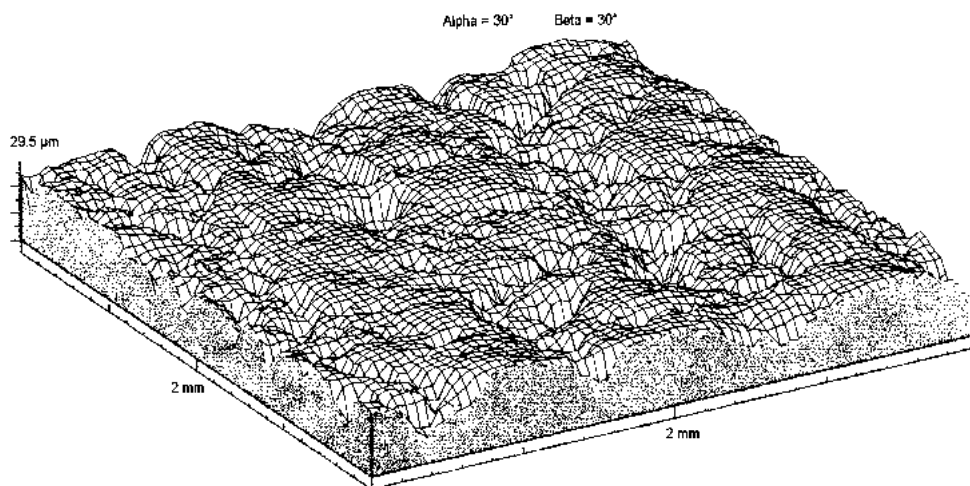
Аксонометричне зображення поверхні деталі після фрезерування та обробки в торувій машині
